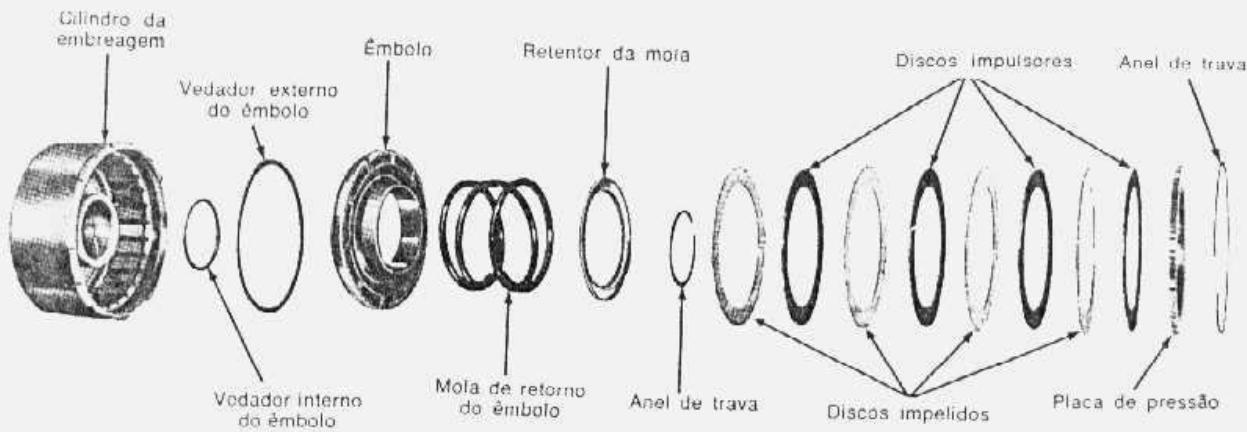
embreagem de marcha-à-ré e alta desmontada - típica
